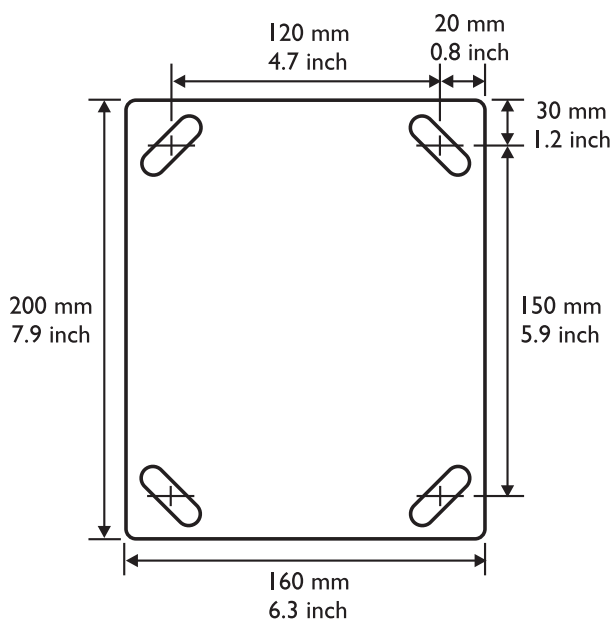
Suporte de montagem de parede LBB 3414/00 com as dimensões e o padrão de perfuração
